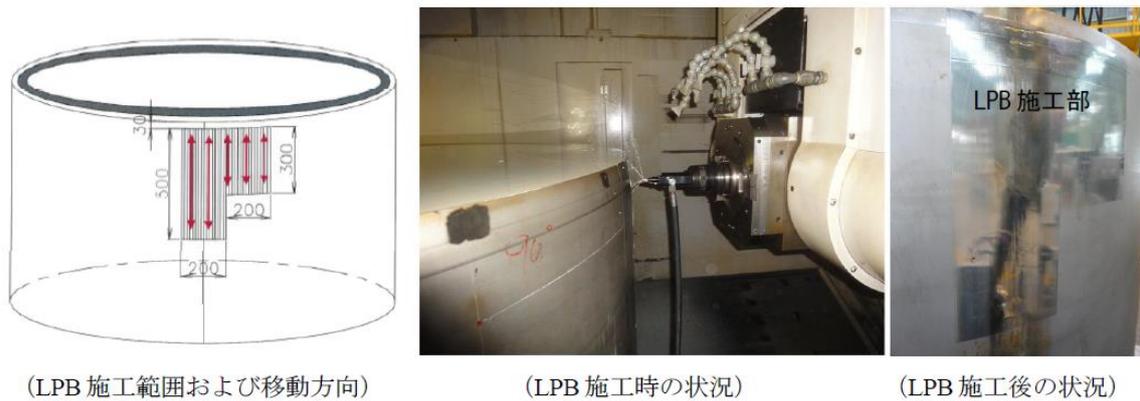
実径大蓋部キャニスタ試験体への LPB 施工状況[12]
